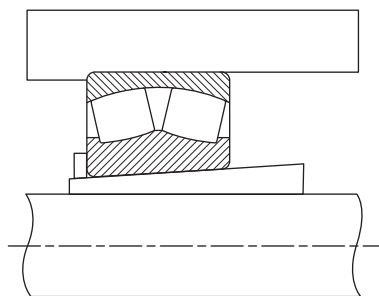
Сферический роликовый подшипник на закрепительной втулке.
